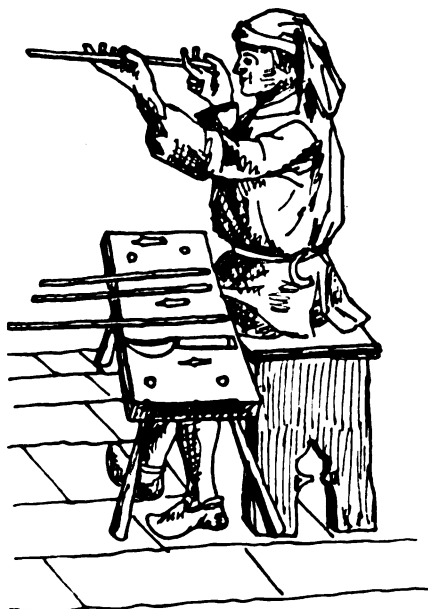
Werkzeugmacher bei der Feilenprüfung im Mittelalter
